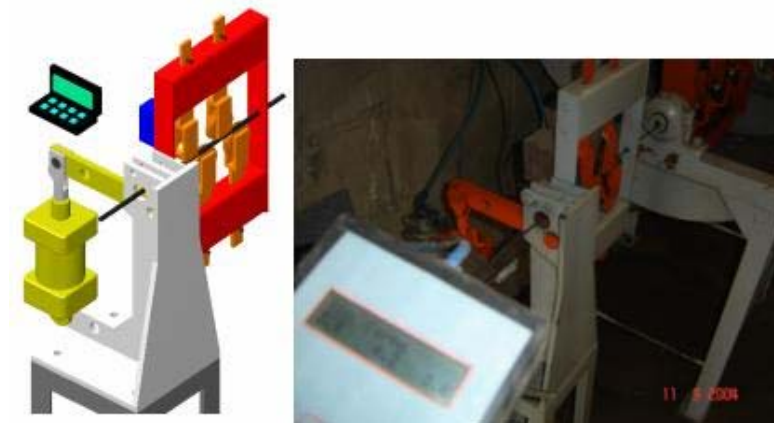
Primeiro projeto da guilhotina automática (P1). (Foto:LEITE FILHO, 2005)
